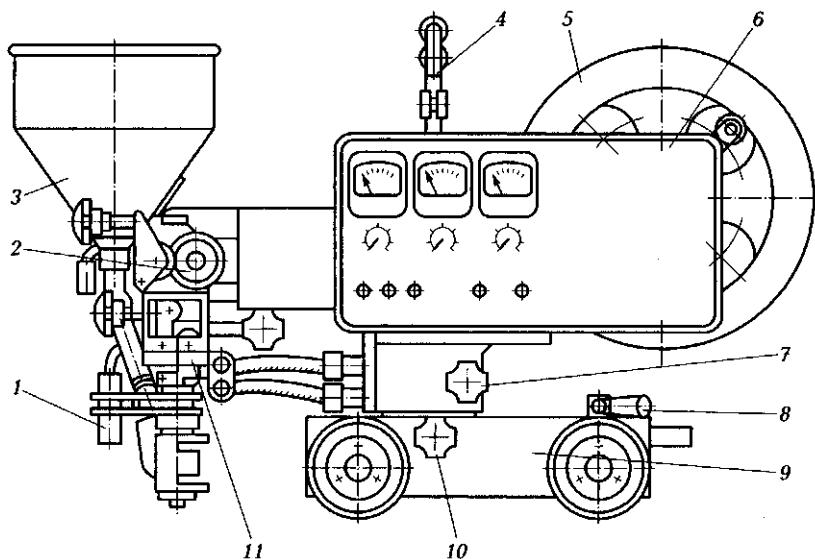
Сварочный автомат тракторного типа серии АДФ:
